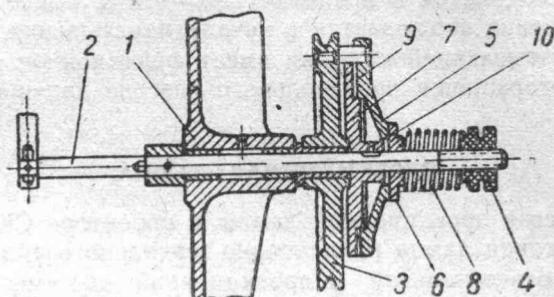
Фрикционная катушка в разрезе: 1 — кронштейн; 2 — вал; 3 — шкив с пальцами; 4 — гайка; 5 — муфта; 6, 7 — фланцы; 8 — пружина; 9 — шайба; 10 — винт
